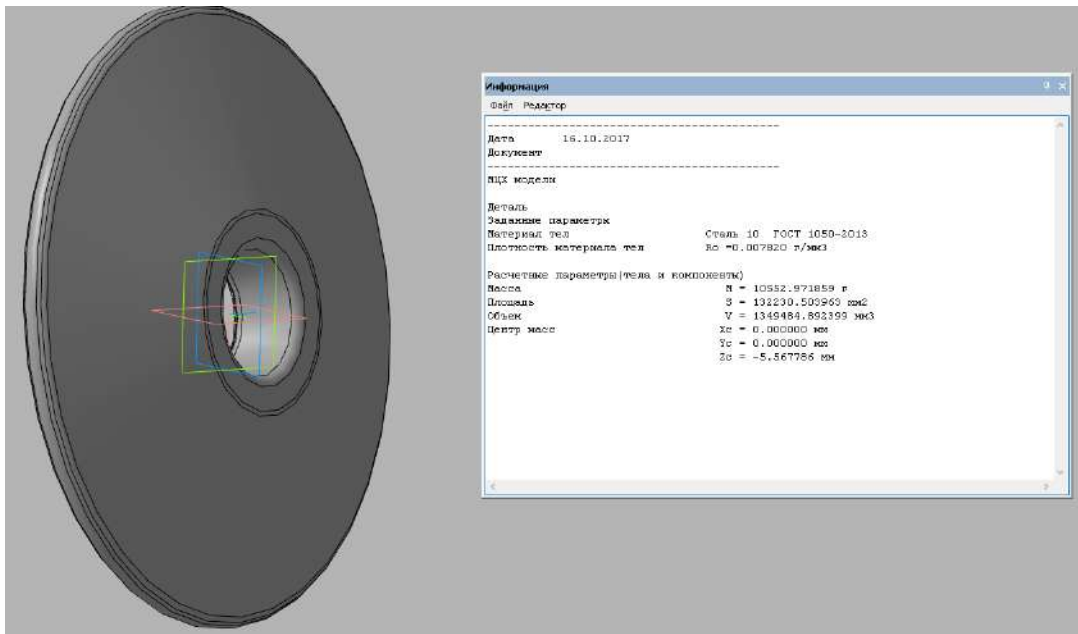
Модель штампованой заготовки на ГКМ
